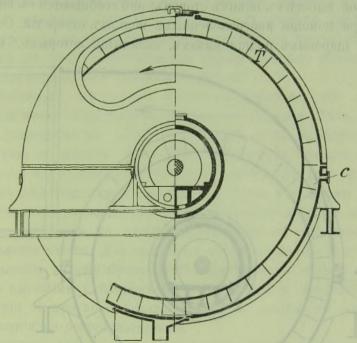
Продольный разрѣзъ чрезъ центробѣжный газоочиститель Theissen.
